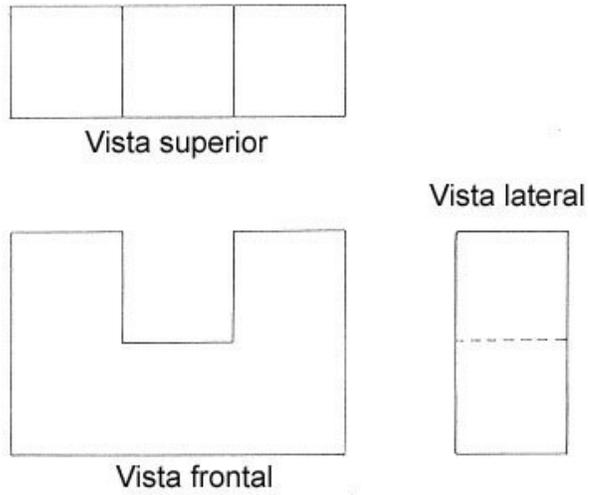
Dibujo con de las tres vistas de la Figura 10.16
